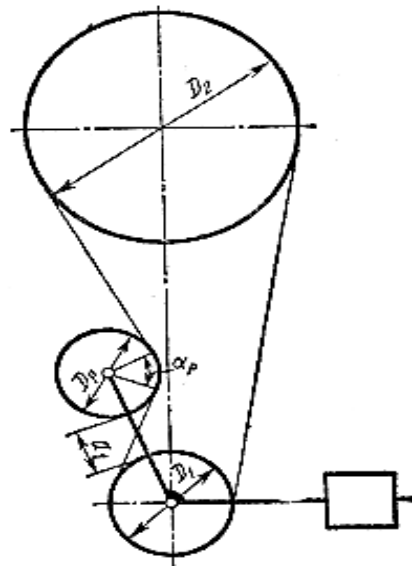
Устройство для натяжения ремней с помощью натяжного ролика
